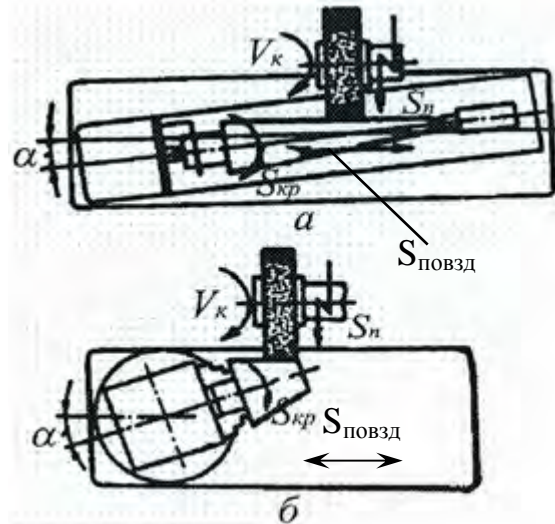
Схеми обробки конічних поверхонь на круглошліфувальних верстатах
